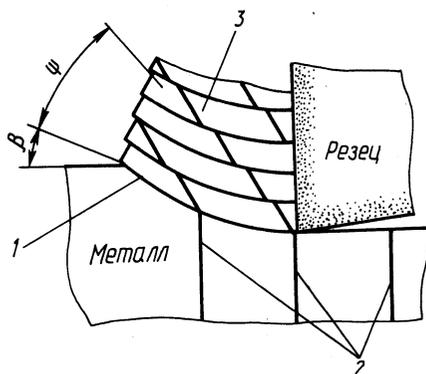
Модель разделения металла фронтами сдвига: 1 – фронт сдвига; 2 – условно выделенный слой металла; 3 – пластинка стружки; β – условный угол сдвига; Ψ – угол текстуры.
